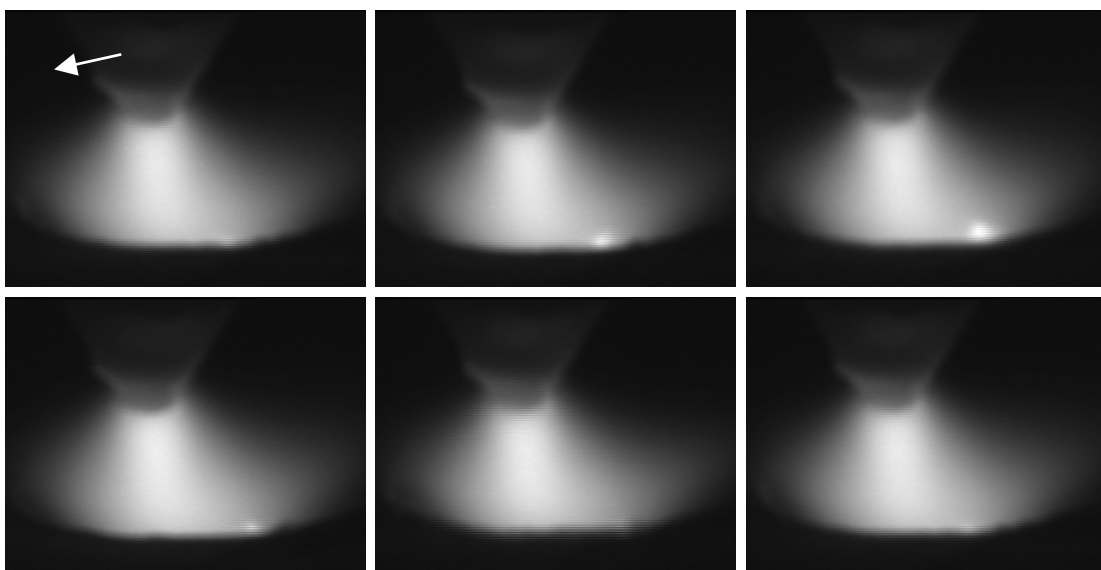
Initiation de la formation du défaut de Puckering en soudage ATIG (220A - 40cm/min)
